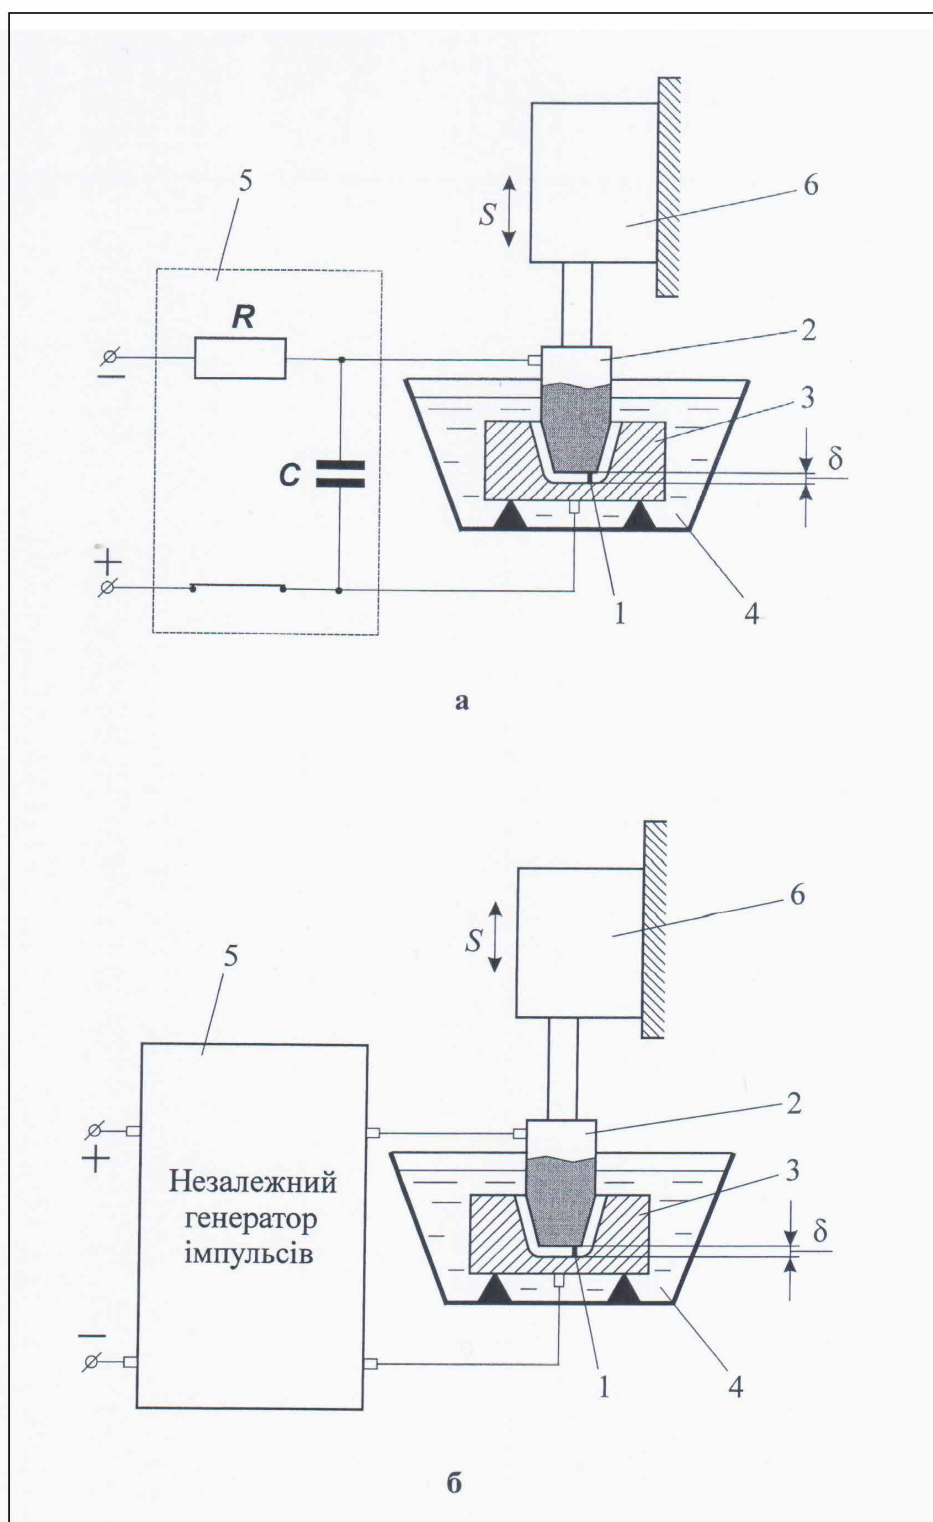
Схеми механічної обробки конічних поверхонь
